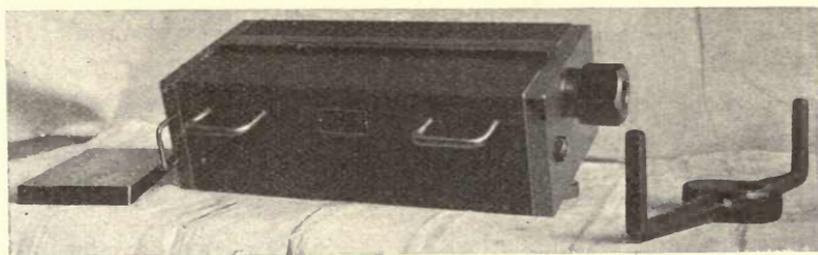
Preßwerkzeug für Wolframstäbe, System W. Gladitz.
